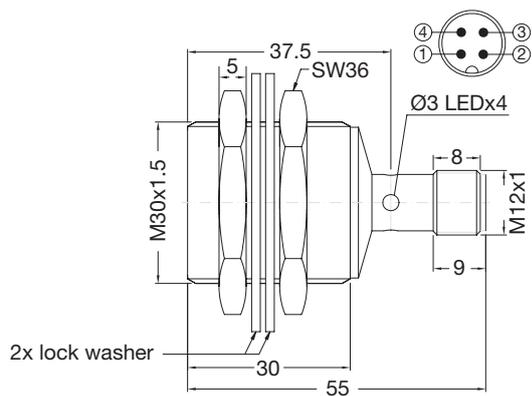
Kurze Ausführung, bündiger Einbau, Steckversion
